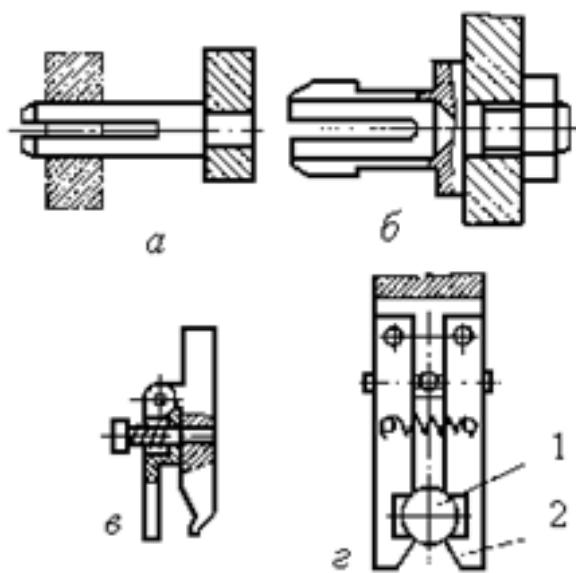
Некеровані захватні пристрої: а – типу пінцета у вигляді пружного розрізного валика, б – типу пінцета у вигляді розрізної пружної втулки, в – типу кліщів з однією рухомою губкою, г – типу кліщів з двома рухомими губками; 1 – заготовка, 2 – робочі елементи
